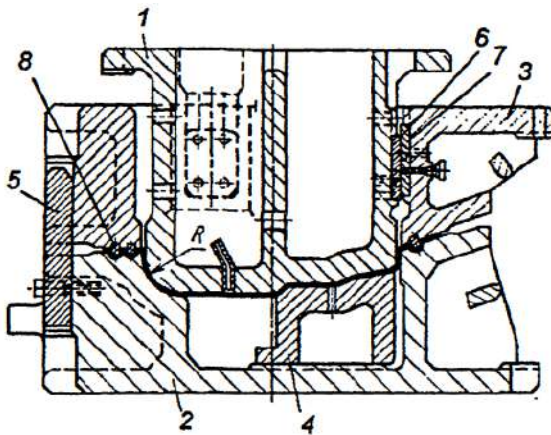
Типова конструкція витяжного штампа подвійної дії
